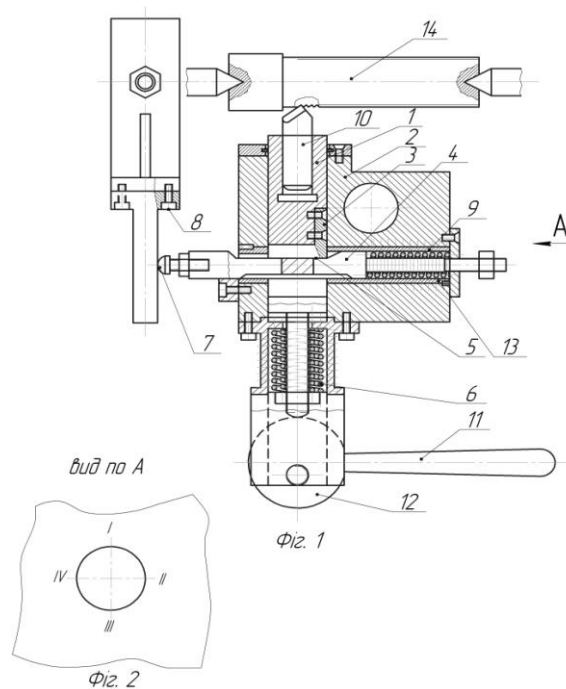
Універсальний пристрій для швидкісного нарізання різі
